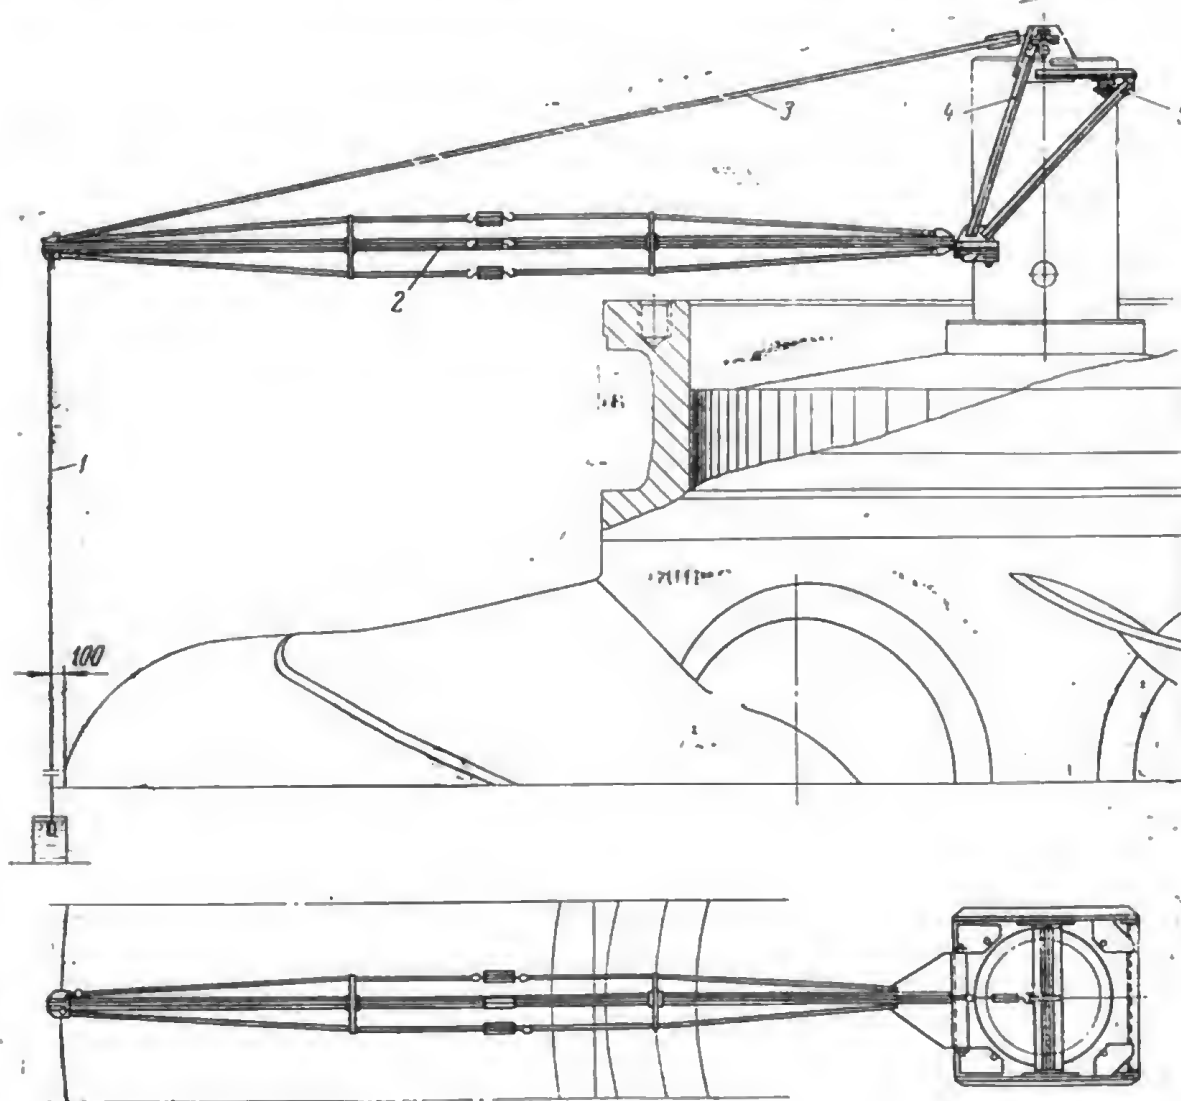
Схема проверки concentричности лопастей рабочего колеса.
